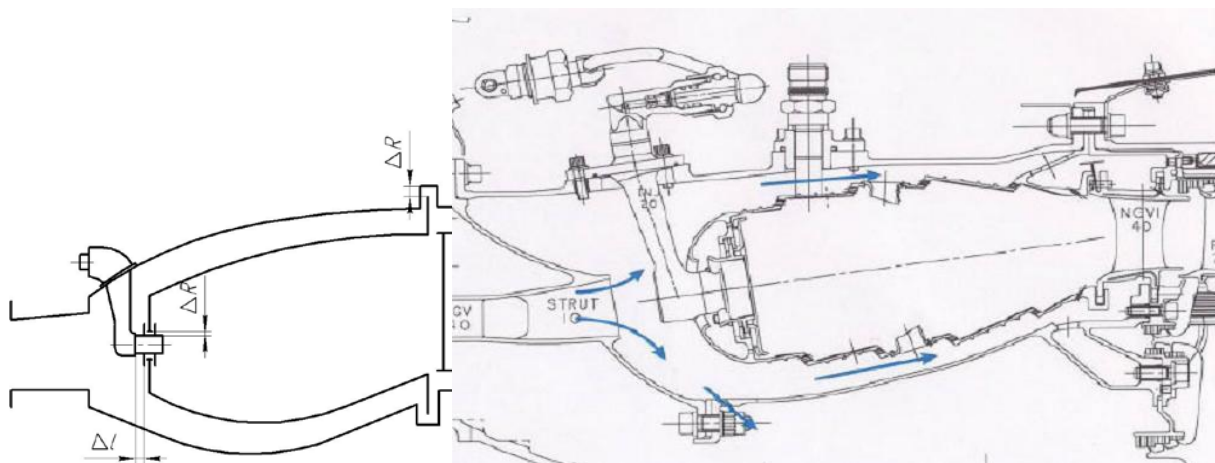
Консольное крепление жаровой трубы (схема и ТРДД BR-715)
